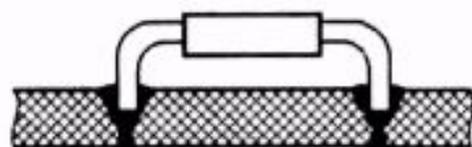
Установка и пайка ЭРИ с плоскими планарными выводами в глухое O-образное монтажное отверстие
